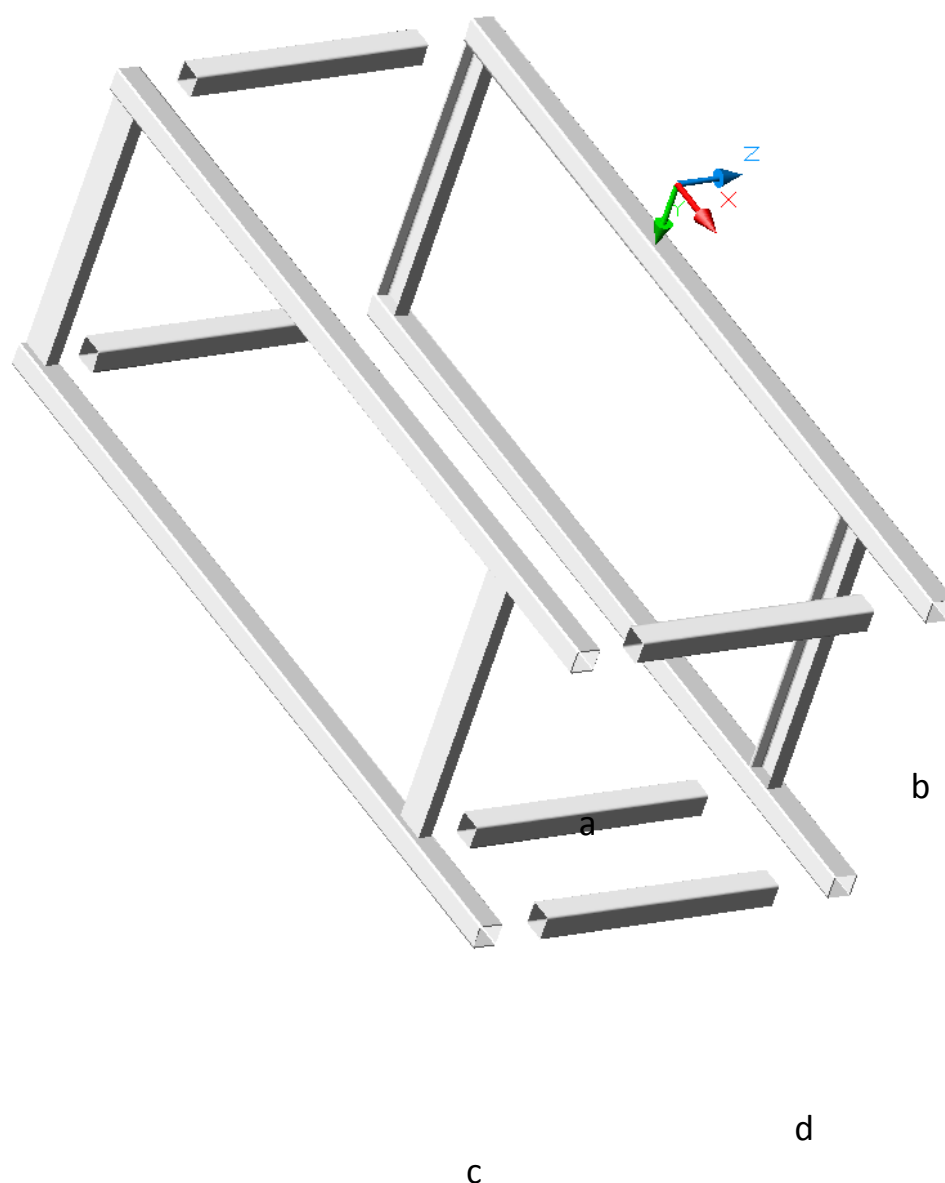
Ensamblaje preliminar de estructura de soporte del compactador
